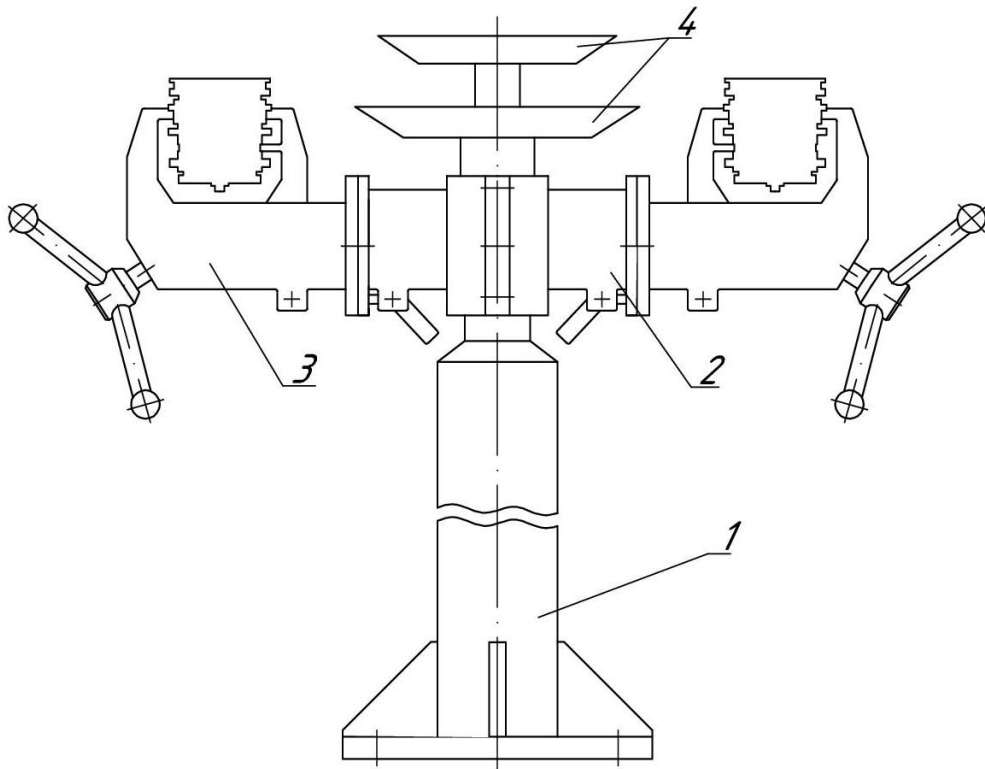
Стенд для ремонту коробки передач типу 2218:
